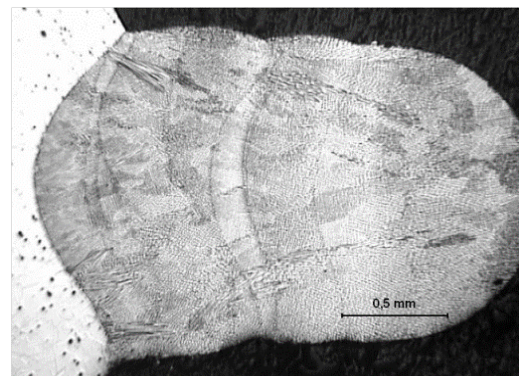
Detalle de la sección transversal del cierre de cuchillas soldado C (3 ipm)
